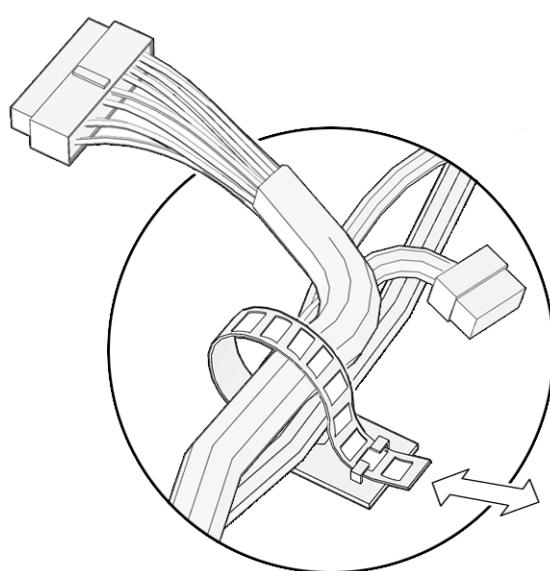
Desserrage des colliers de serrage des câbles d'alimentation E/S
